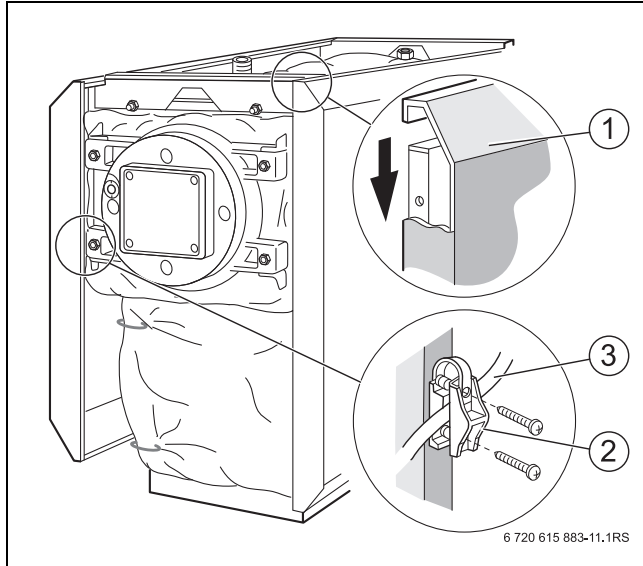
Установка боковых стенок и прокладка кабеля горелки
